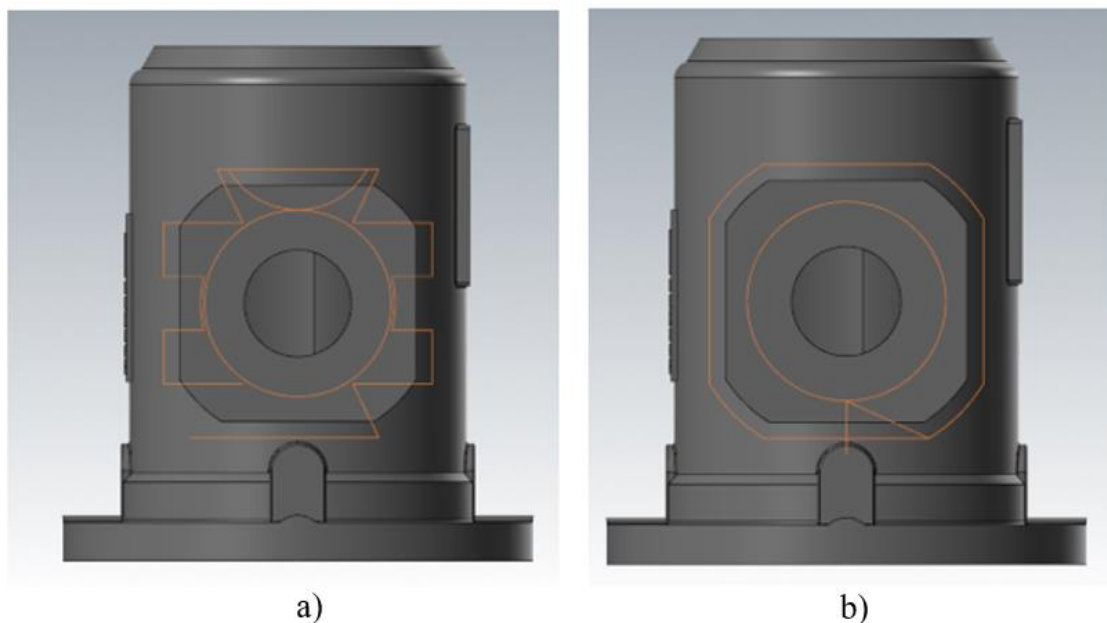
Estratégias de maquinagem *Mastercam* aplicadas à caixa de terminais: a) Zig Zag; b) Constant Overlap Spiral.
